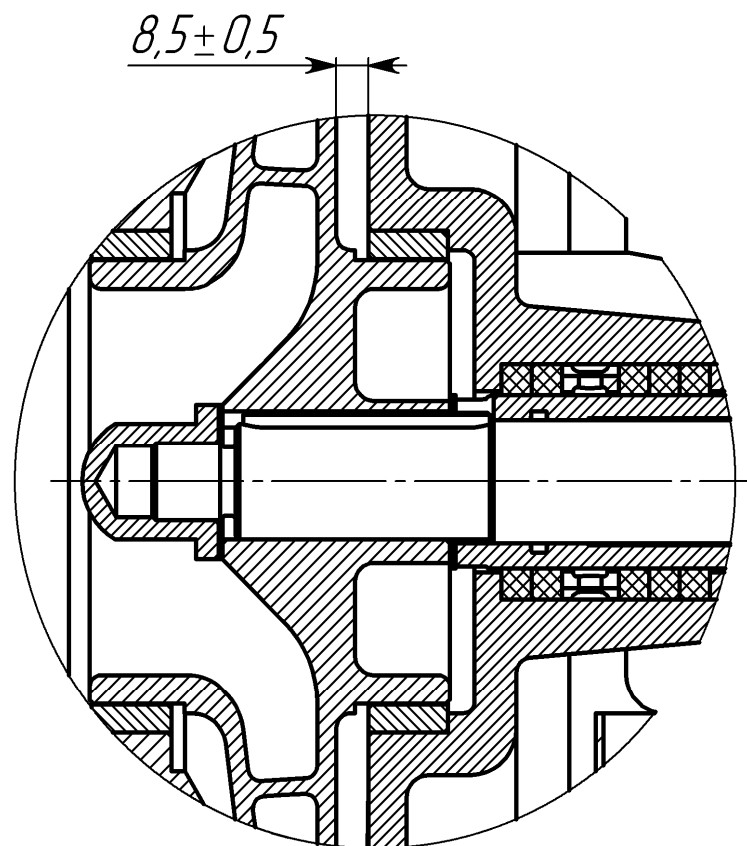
Установочный размер колеса рабочего для насоса X-100-65-250
